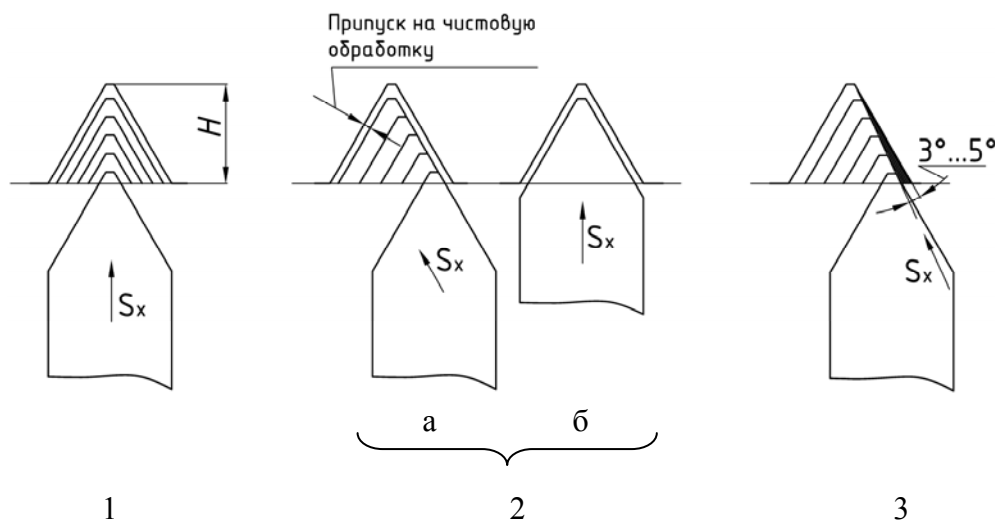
Схемы срезания припуска при нарезании резьбы резьбовыми односторонними резцами $P \leq 2,5$ мм: радиальная подача; 2, 3. $P > 2,5$ мм: а) черновой проход, б) чистовой проход.
